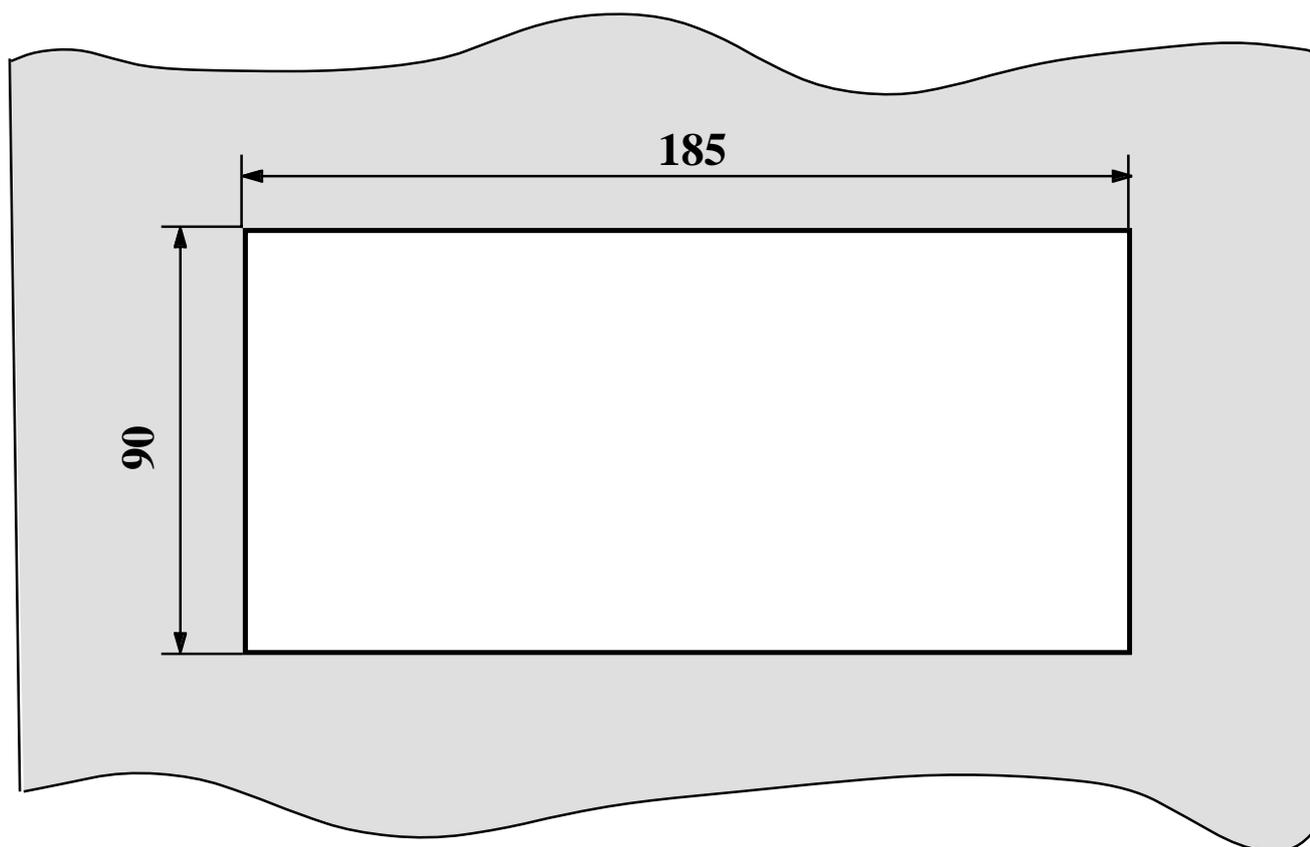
DIMENSIONI DELLO SCASSO PER IL MONTAGGIO MECCANICO
